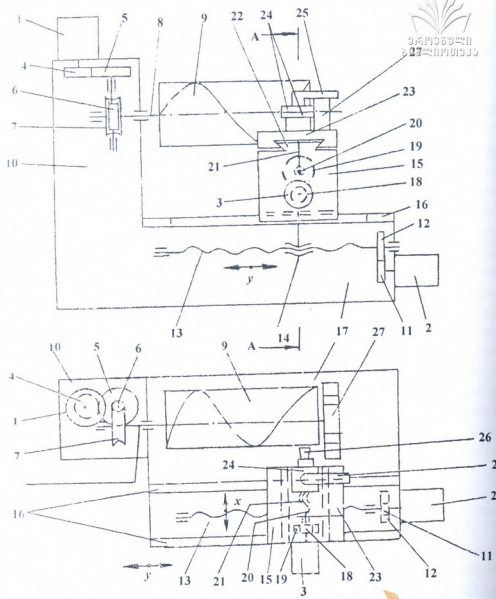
Кинематическая схема станка с ЧПУ для нарезания цилиндрических червяков
